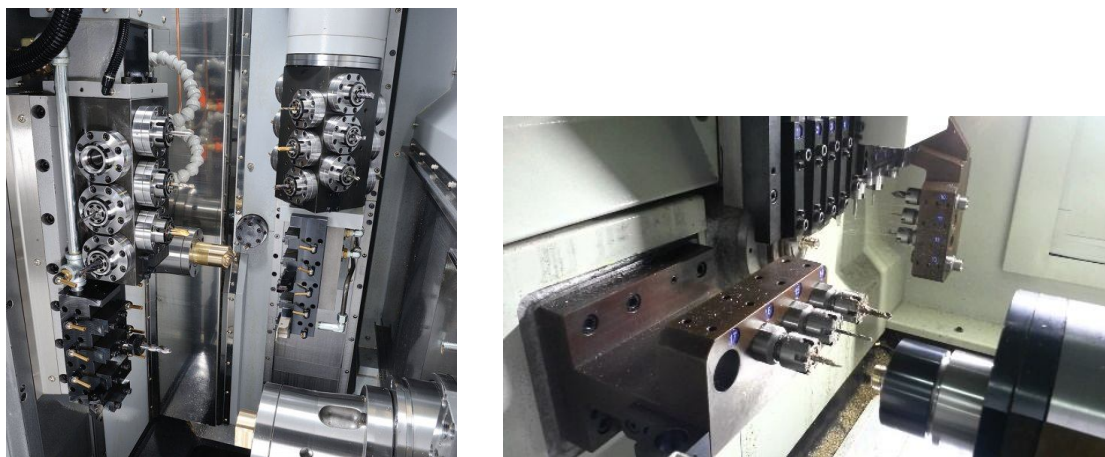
Двухшпиндельные станки с инструментальными консолями
